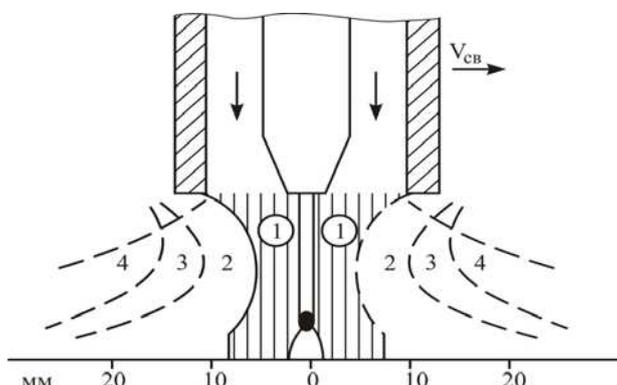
Состав струи углекислого газа, истекающего из сопла сварочной горелки: 1 – 100 % CO₂; 2 – CO₂ + 10 % воздуха; 3 – CO₂ + 60 % воздуха; 4 – CO₂ + 80 % воздуха
